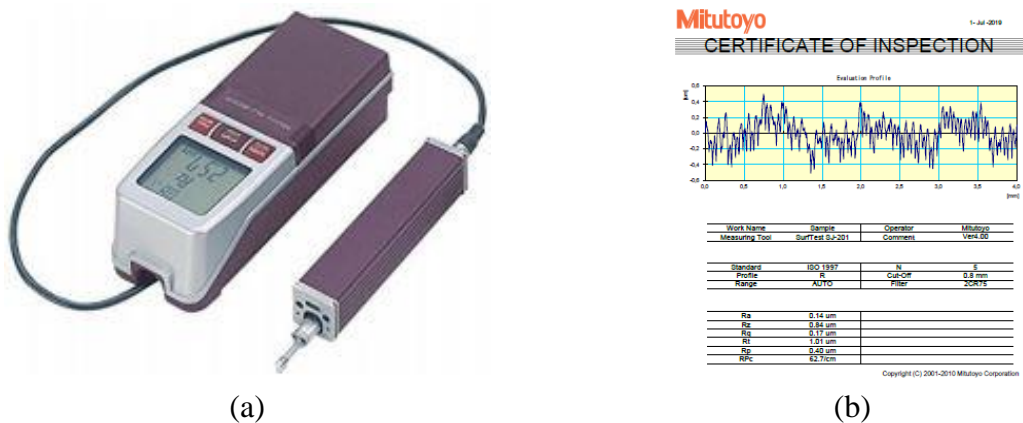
Medição de rugosidade: (a) rugosímetro SJ-201P; (b) certificado de inspeção.
